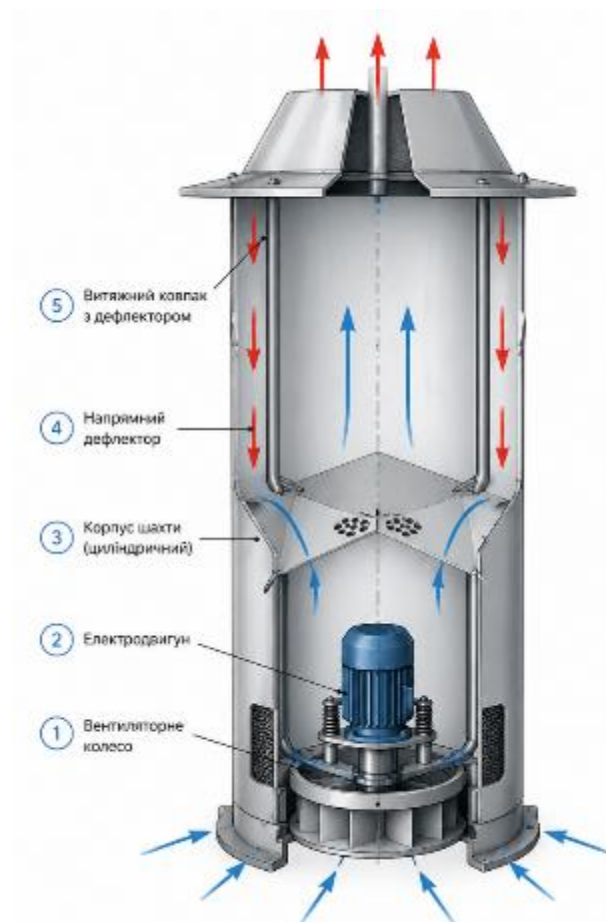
Конструкція припливно-витяжної установки ПВУ
